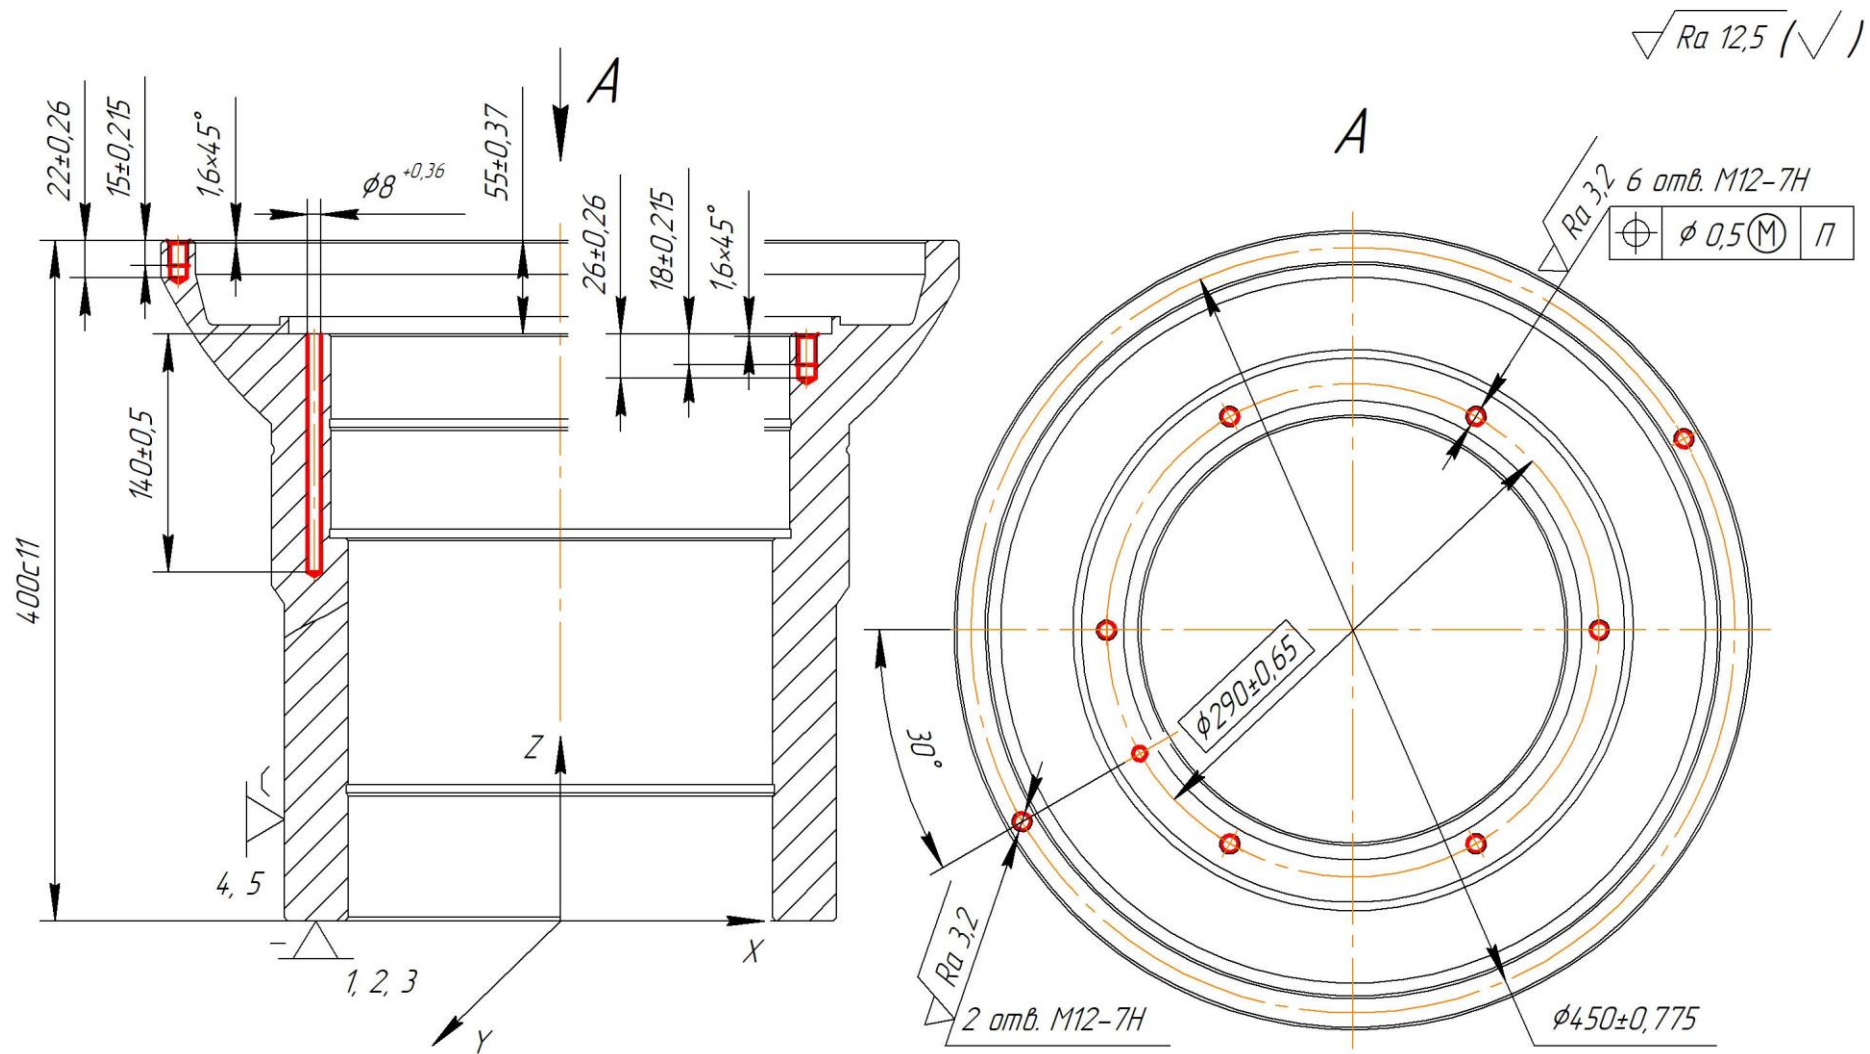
Схема базування заготовки на операції 050 (установ А)
